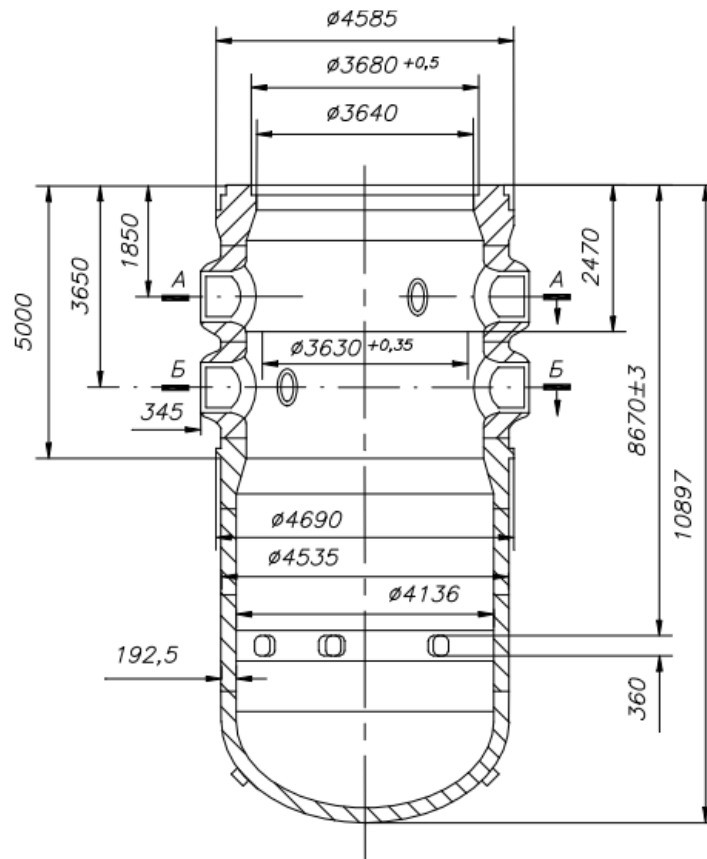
Корпус реактора ВВЭР- 1000
